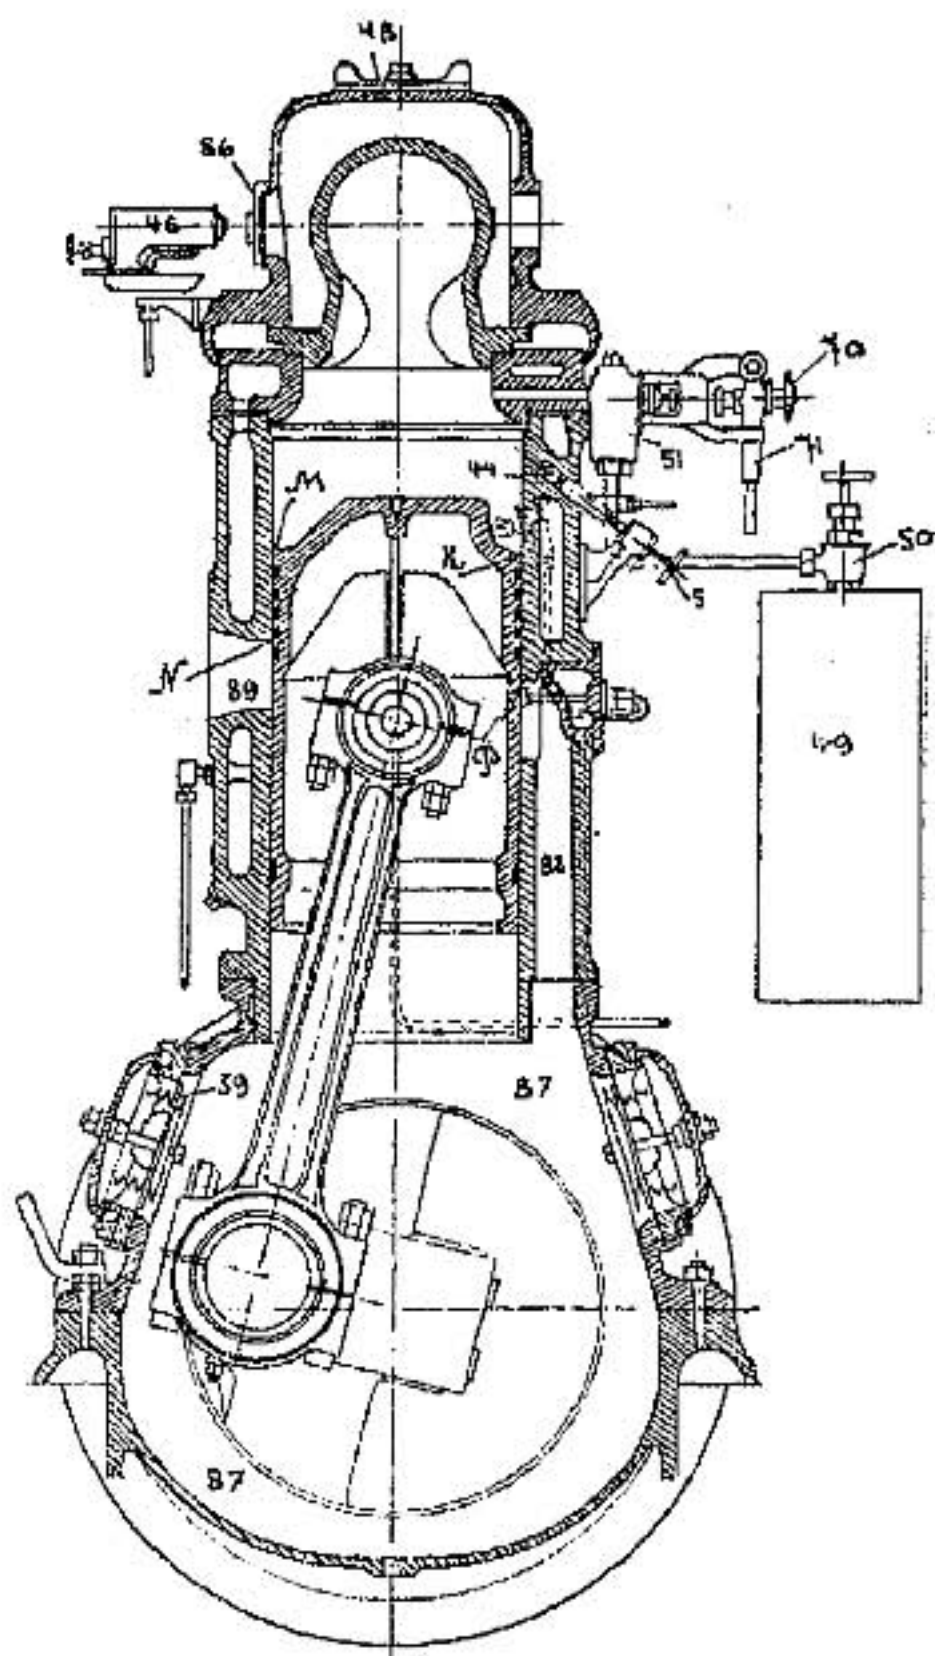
Поперечный разрез нефтяного двигателя Ижорского Завода.
